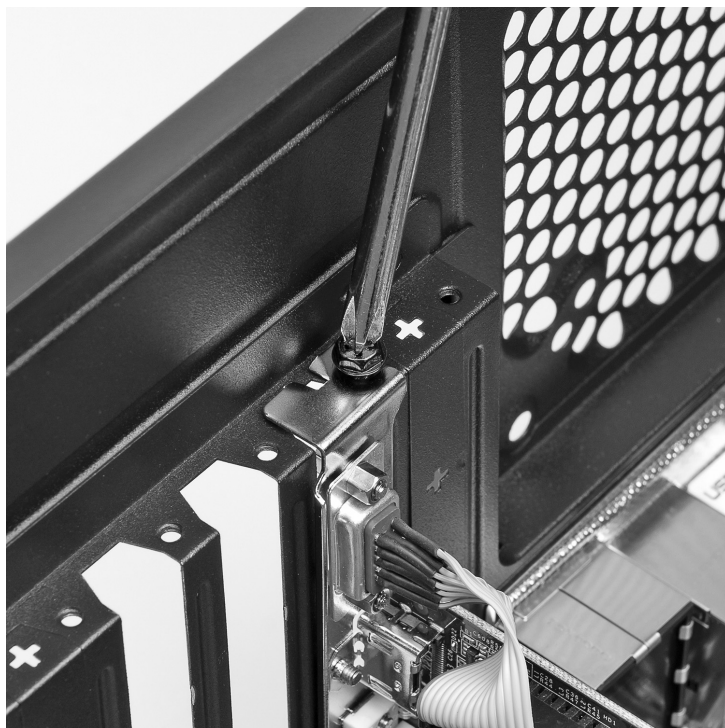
Schrauben Sie Steckkarten immer gut fest.
